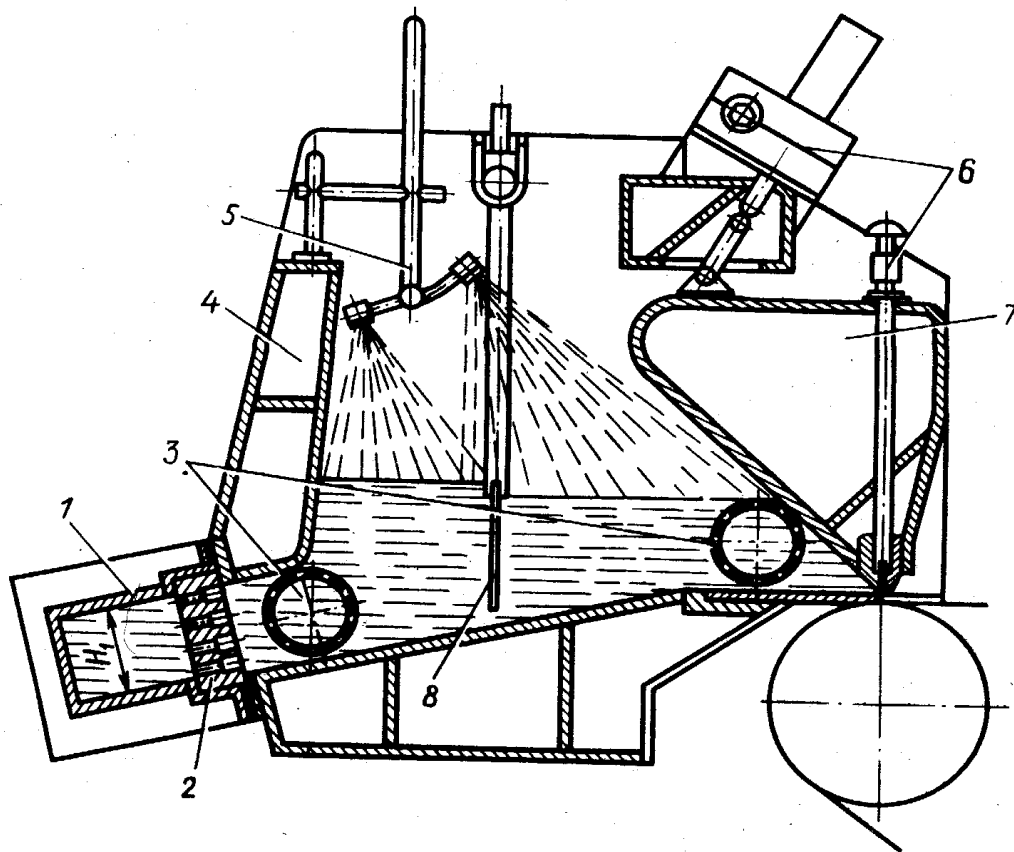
Напiрний ящик вiдкритого типу: 1 – перфорована плита; 2 – колектор-потокорозподiлювач; 3 – перфорований валик; 4 – корпус ящика; 5 – пiногасник; 6 – механiзм регулювання щiлини; 7 – передня стiнка; 8 – перегородка.
